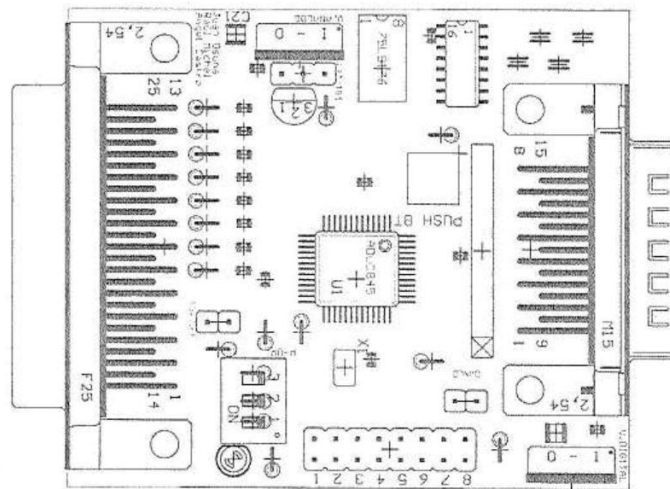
PCB:Tarjeta de adquisición, máscara de componentes.
